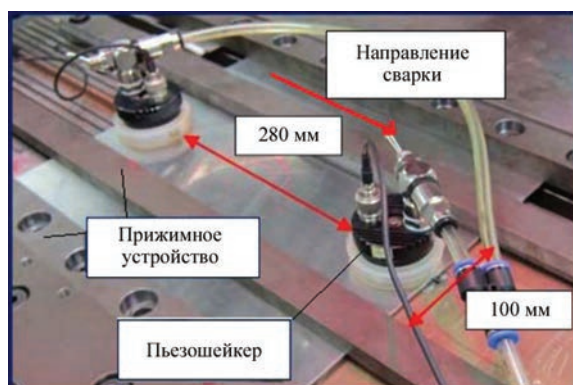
Вид образцов с зафиксированными пьезошейкерами перед лазерной сваркой
